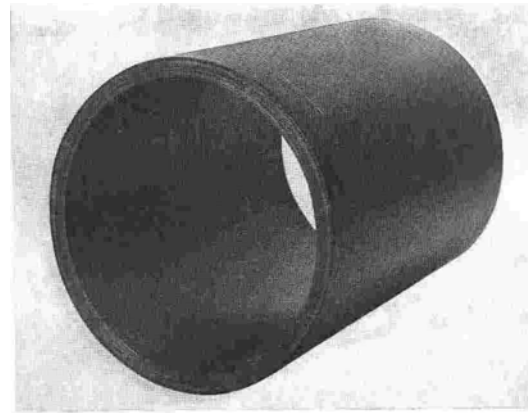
Druckkörper aus dickwandigem Schichtsperrholz.
